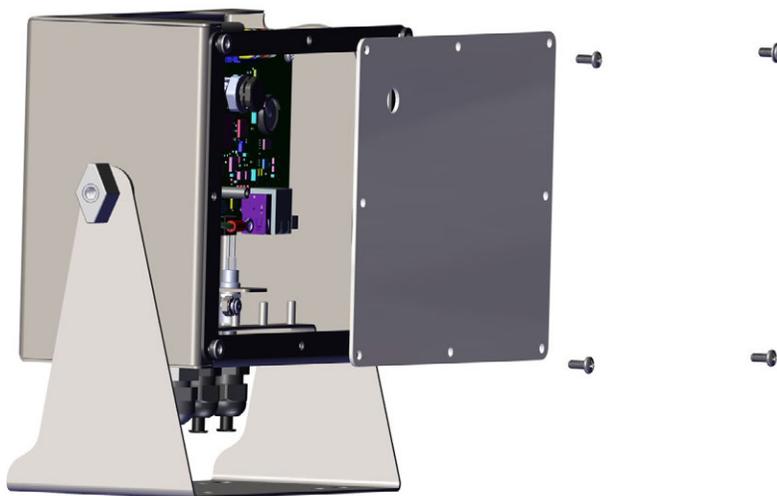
Rückplatte der Universal-Montagehalterung entfernen
